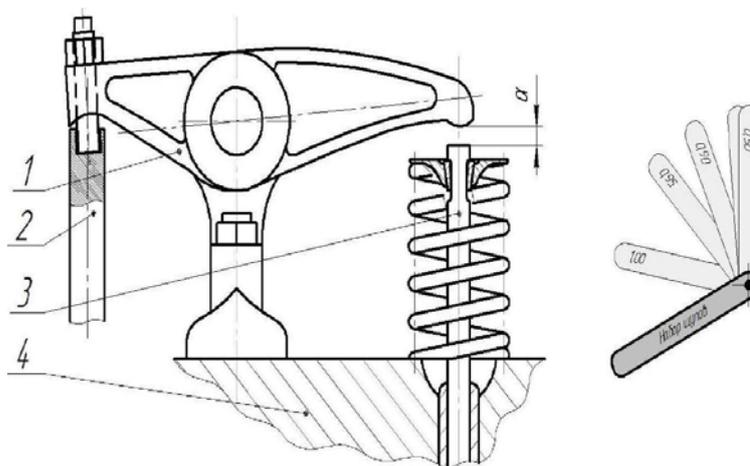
Определение теплового зазора в клапанном приводе двигателя с нижним расположением распределительного вала 1 - Клапанный рычаг (коромысло); 2 - Штанга; 3 - Клапан; 4 - Крышка цилиндра; а - Тепловой зазор в клапанном приводе
